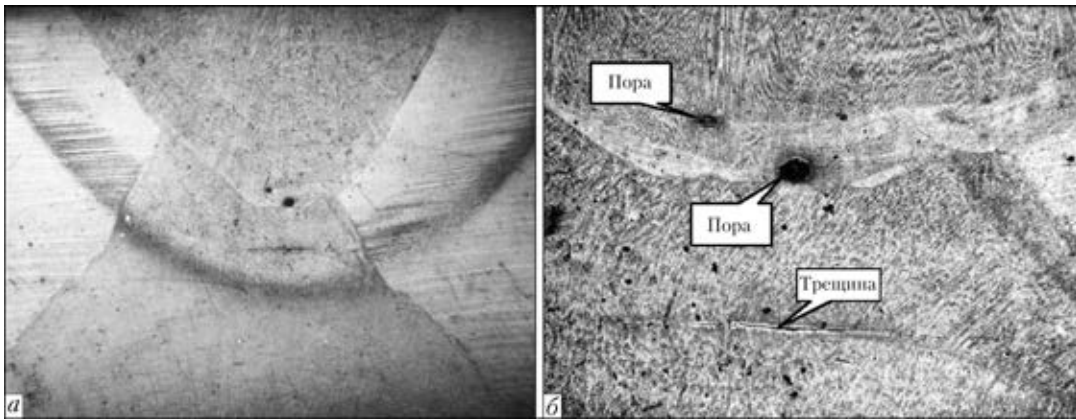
Макроструктура сварного шва стали WELDOX 1300: *a* — общий вид ($\times 10$); *б* — холодные трещины и поры в участке металла ЗТВ ($\times 50$)
